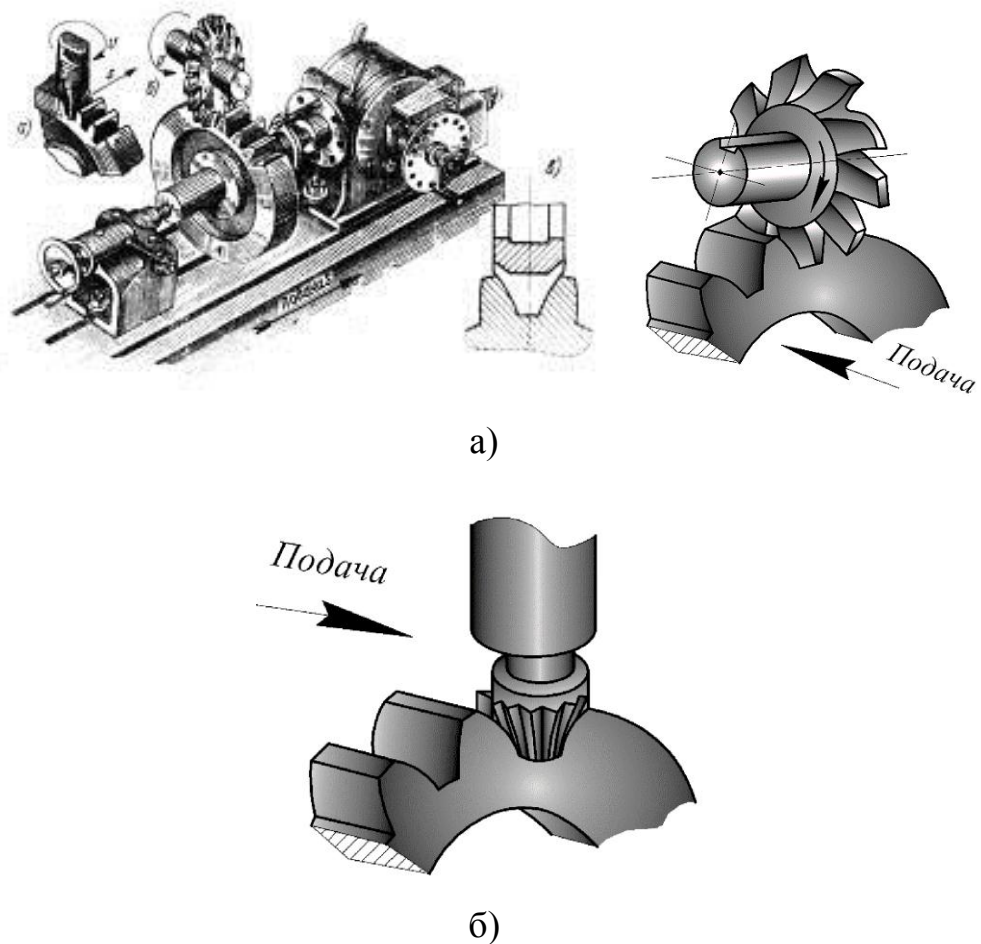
Фрезерування профільних поверхонь методом копіювання:
